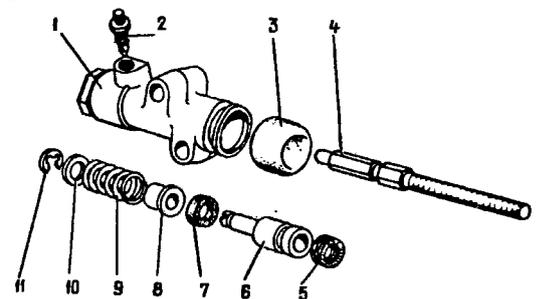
Детали цилиндра привода выключения сцепления (рабочего цилиндра): 1 - корпус; 2 - штуцер; 3 - колпачок; 4 - толкатель; 5 - уплотнительное кольцо; 6 - поршень; 7 - уплотнительное кольцо; 8 - тарелка; 9 - пружина; 10 - шайба; 11 - стопорное кольцо
